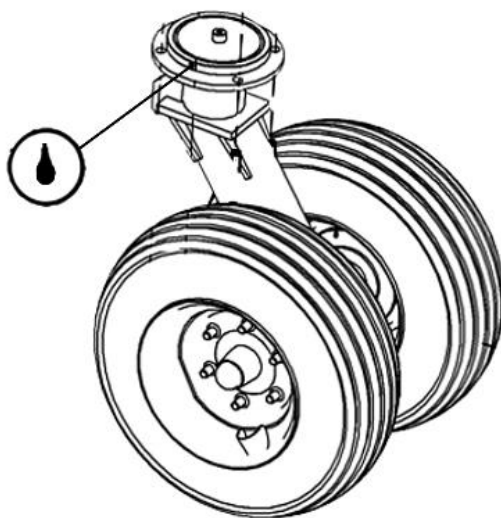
Смазка переднего шасси нового образца.
